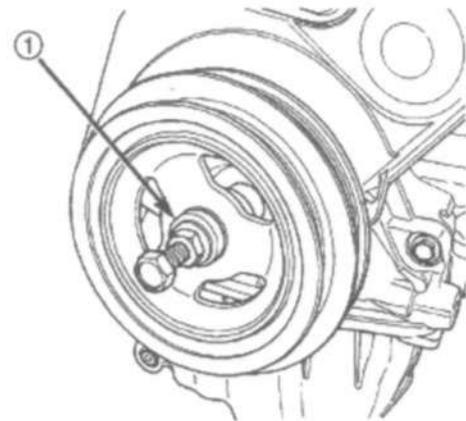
Гаситель вибрации коленчатого вала – типовая установка
